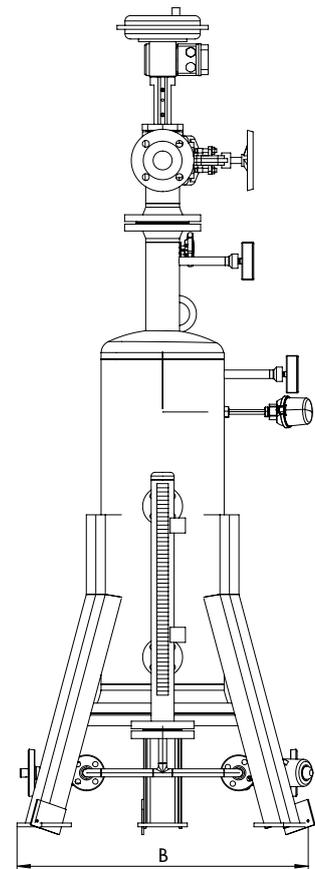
Maßbilder, Wasserbadkühler Typ 7110 mit Gestell · Wasserbadkühler Typ 7110 mit Füßen
